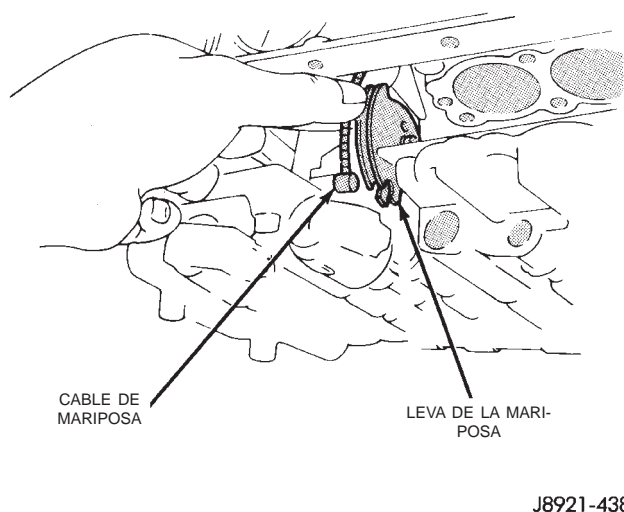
Desmontaje e instalación del cable de mariposa de la transmisión
